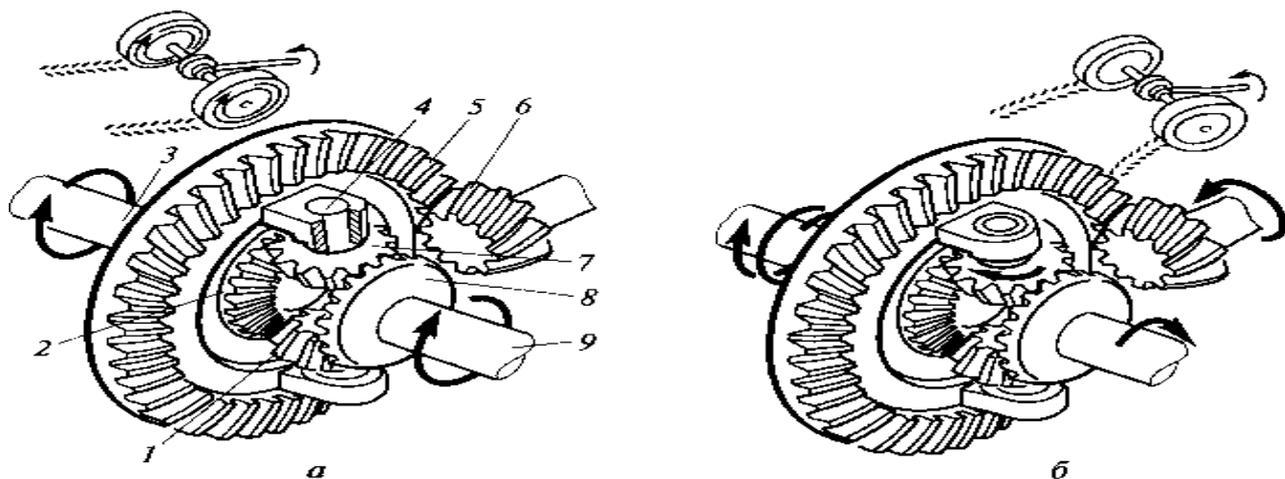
Дифференциал: а — движение по прямой; б — при повороте на закруглении дороги; 1, 7 — сателлиты; 2, 8 — полуосевые шестерни; 3, 9 — полуоси; 4 — палец; 5 — ведомое зубчатое колесо; 6 — ведущее зубчатое колесо
